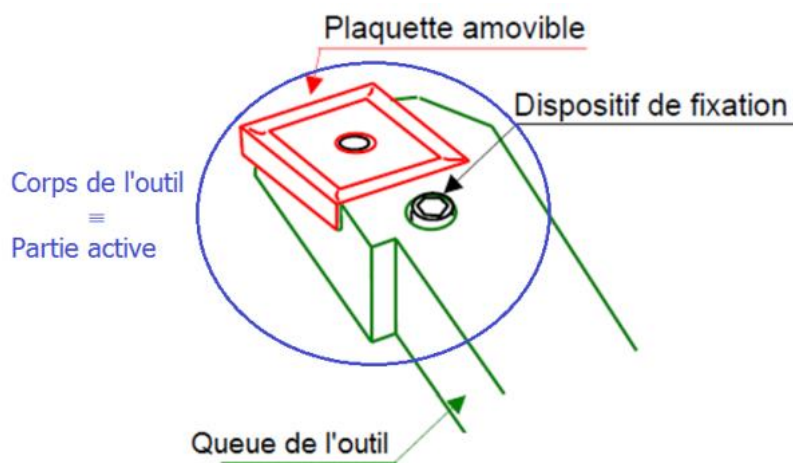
Les compositions d'un outil à charioter plaquettes en carbure [9].
